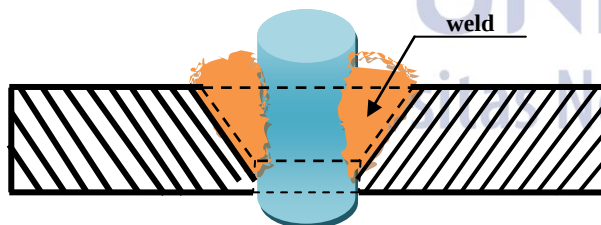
Penampang Specimen Las S35C (Tampak Atas)
